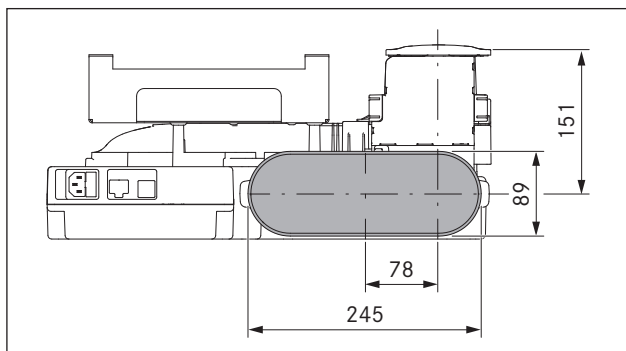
Rozmery pripojenia potrubia PKA s kolenovou prechodkou
